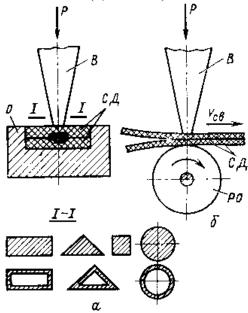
Схема контактной ультразвуковой сварки: а – прессовая; б – шовная; В – волновод; СД – свариваемые детали; РО – ролик опора.
